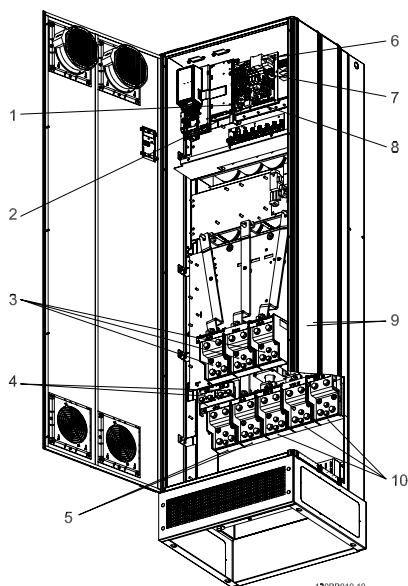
Compact IP 00 (Chassis) met werkschakelaar, zekering en RFI-filter, framegrootte D4
